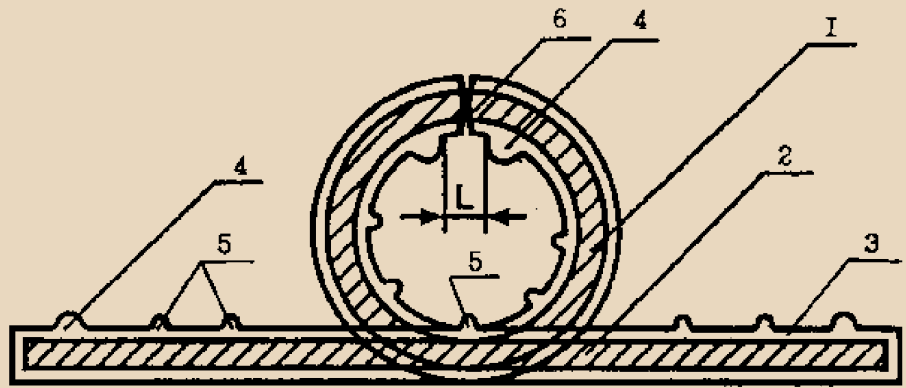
Трубы 1 \varnothing 20–60мм предлагается сваривать из ленты 2 с ПК 3 и продольными утолщениями ПК 4 (до 40–60мкм) для протекторной защиты в транспортируемых средах зоны L термического воздействия сварного шва. Но для больших размеров труб для увеличения долговечности выгодно наносить дополнительные утолщения ПК 5 с увеличением массы протектора.
